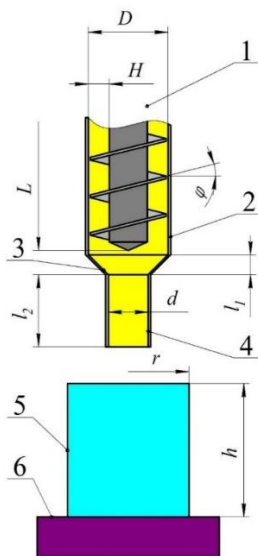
Схема дозатора із нерухомим патрубком: 1 – шнек; 2 – корпус; 3 – конфузор; 4 – патрубок; 5 – тара; 6 – зважуючий елемент
